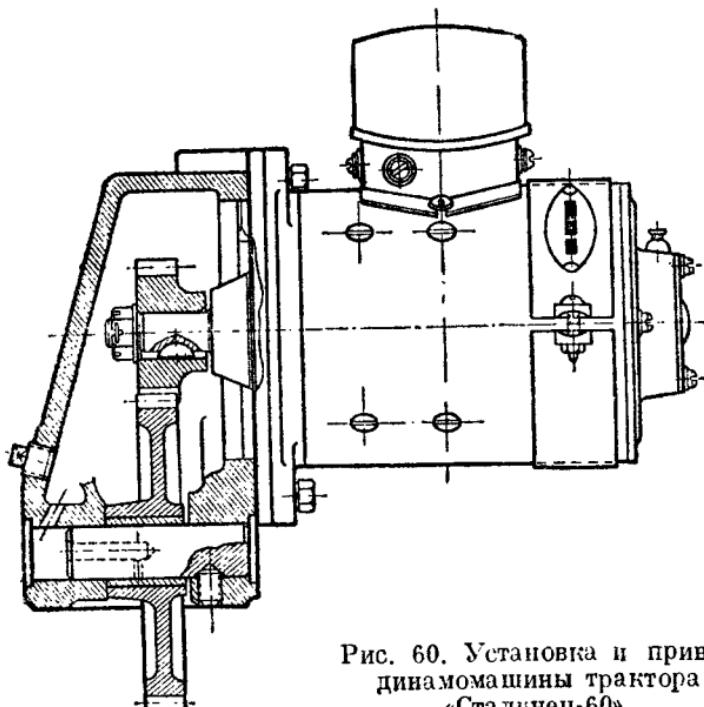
Установка и привод динамомашины трактора «Сталинец-60».
